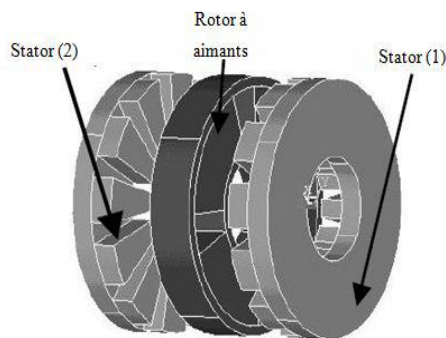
Descriptif de la machine à flux axial stator externe. [14]
